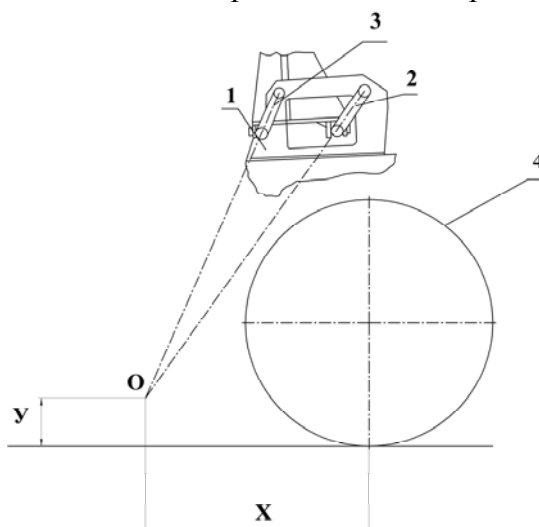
Схема шарнирно-рычажного сцепного устройства
